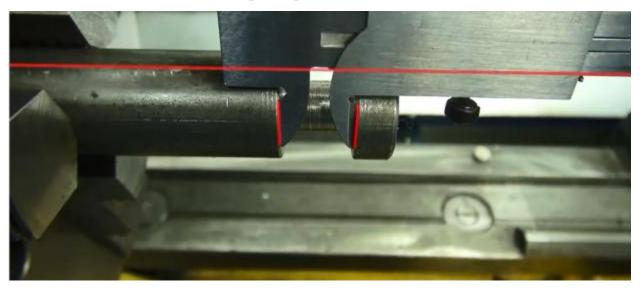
Положения штангенциркуля при измерениях внутренних длин
